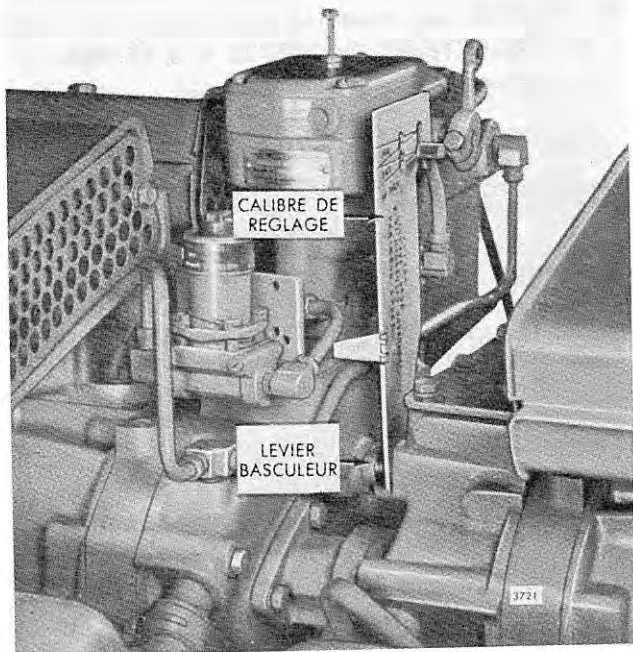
Jauge n° J.21304 placée sur le régulateur
